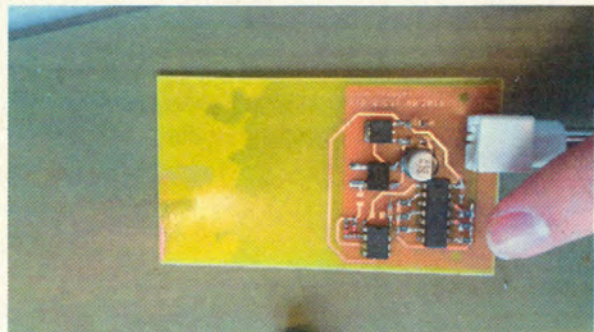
Händisch bestückte Platine (hier für einen Line-Trigger).
